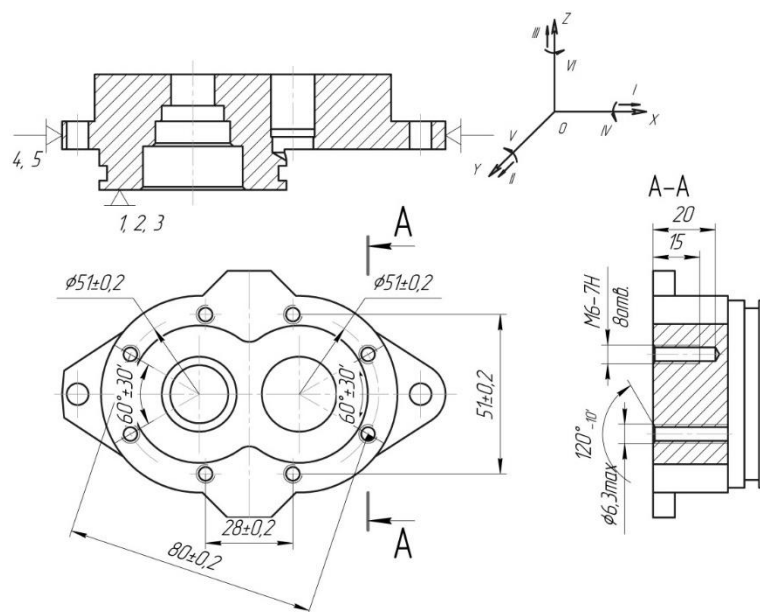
Схема базування заготовки в самоцентруючих призмах
